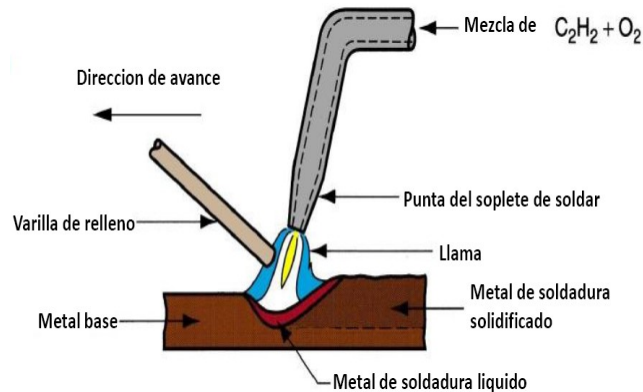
Proceso de soldadura oxiacetilénica.
